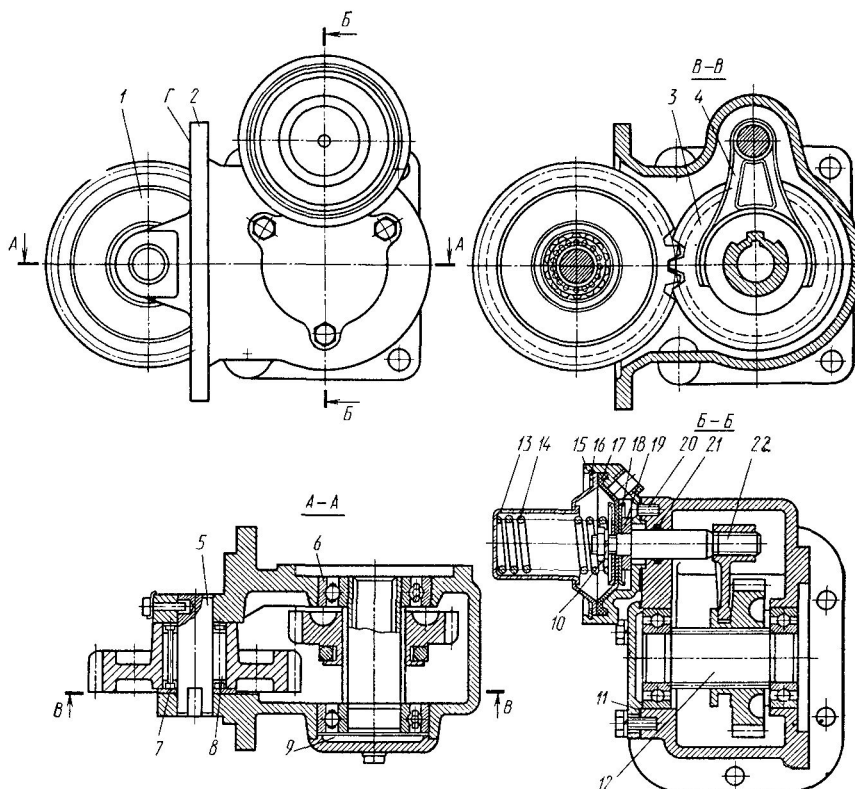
Коробка отбора мощности с постоянным зацеплением промежуточного зубчатого колеса с колесом коробки передач
